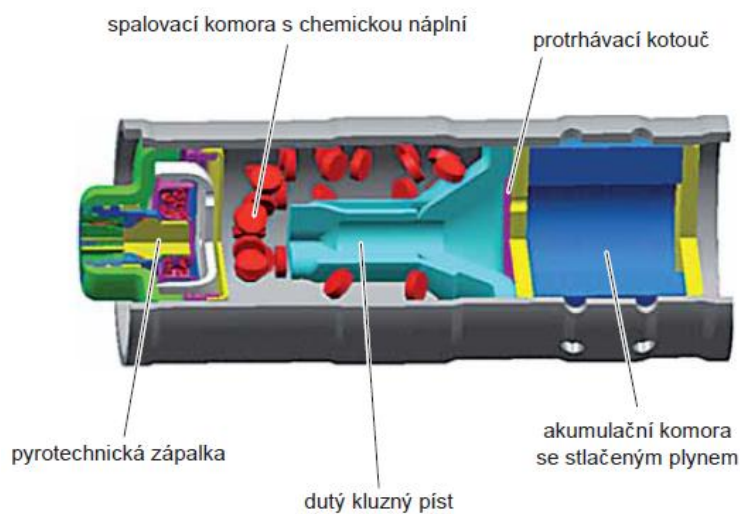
Generátor plynu pro airbag s pyrotechnickou zápalkou [1]
